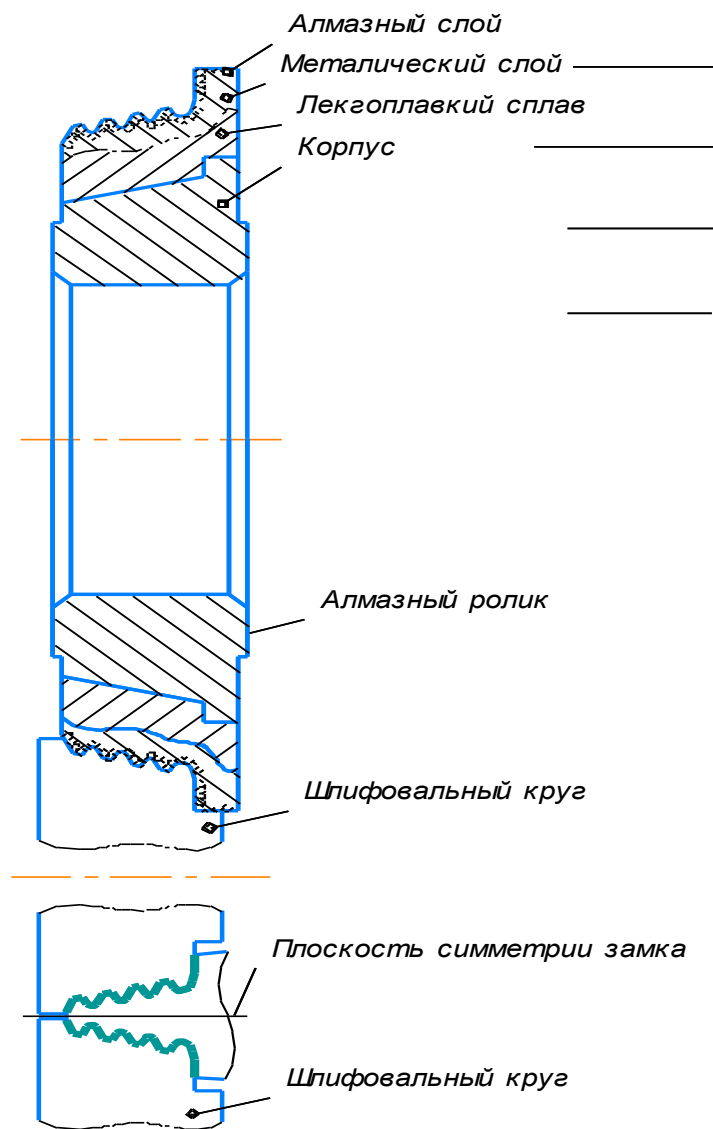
Схема обработки замка лопатки ёлочного профиля
